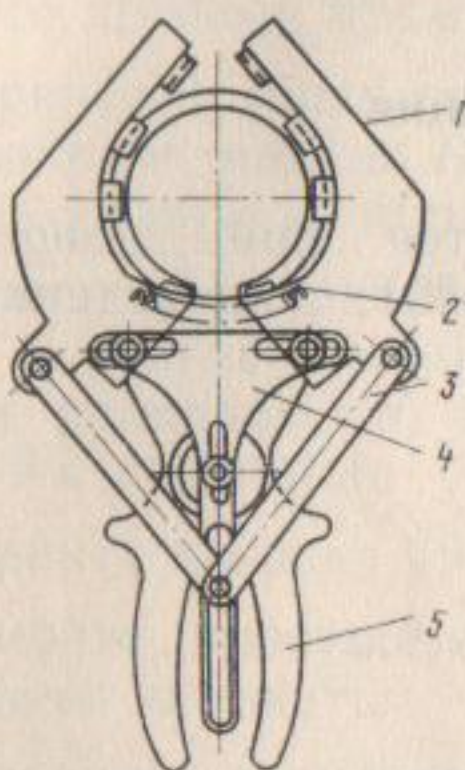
Съемник для снятия и установки поршневых колец компрессора:
